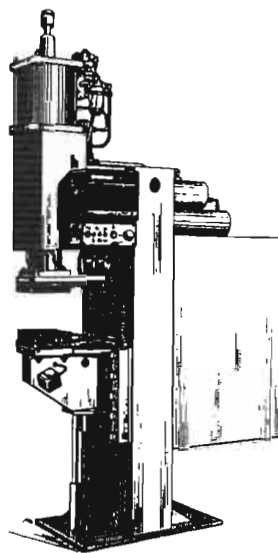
Машина для рельефной сварки типа МР-4020
